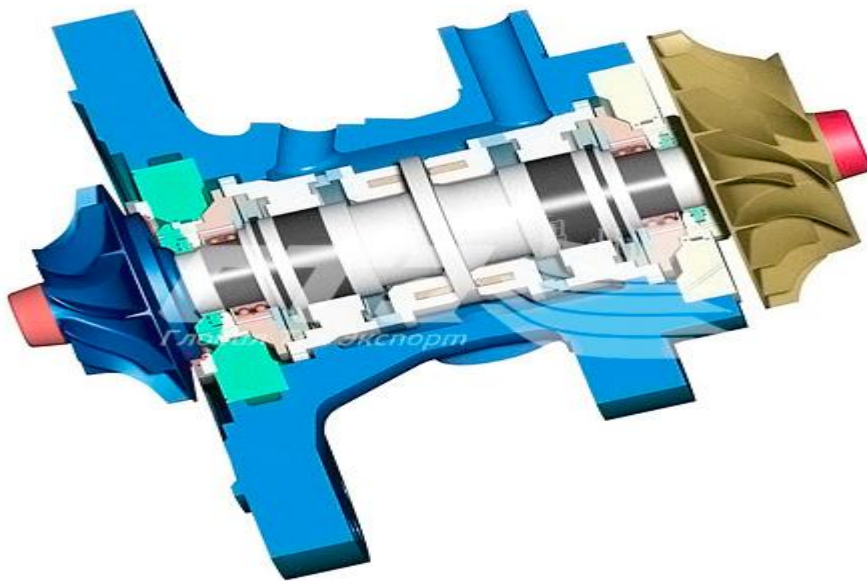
Магнитный радиальный подшипник (разрез модуля)
